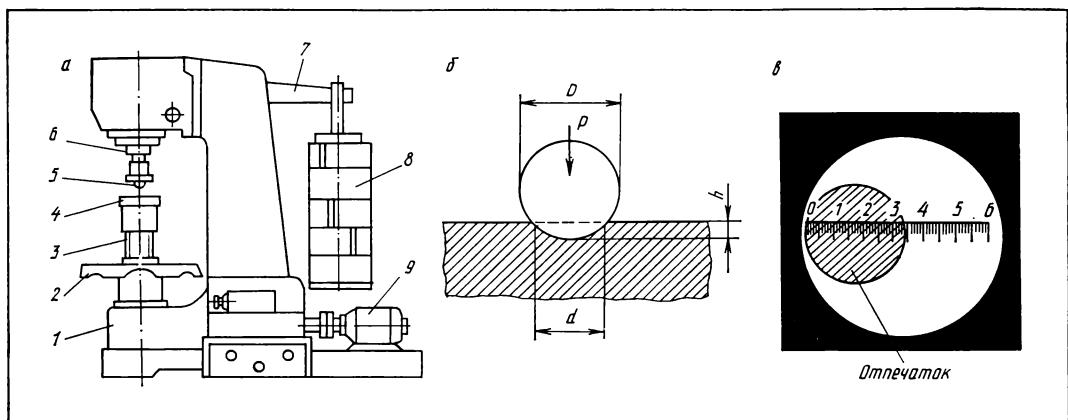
Устройство твердомера (пресс Бринелля):
